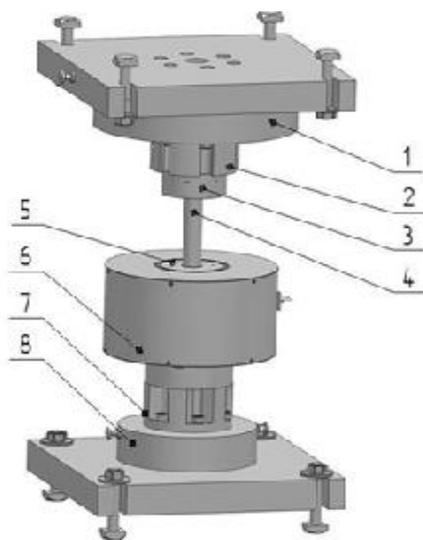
Пресс-оснастка для горячего прессования (экструзии) брикетов в пруток: 1 – плита верхняя; 2 – держатель штемпеля; 3 – фланец; 4 – пресс-штемпель; 5 – контейнер; 6 – печь кольцевая; 7 – корпус матрицы; 8 – плита нижняя
